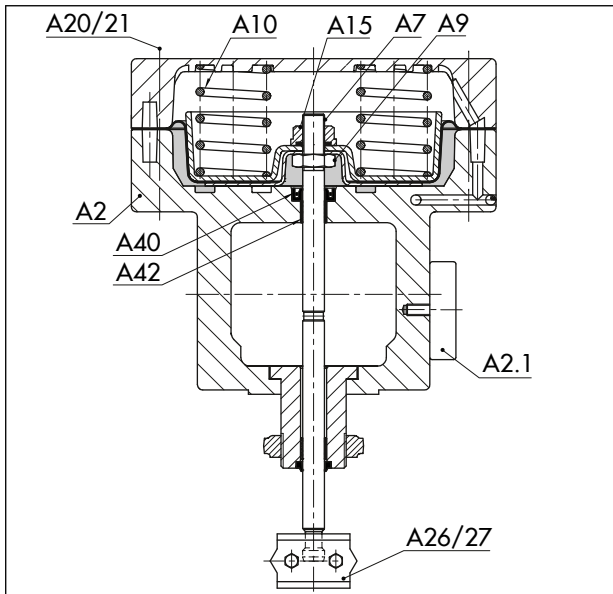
Atuador Tipo 3271-5, desenho que apresenta um exemplo com área do atuador de 120 cm<sup>2</sup>
